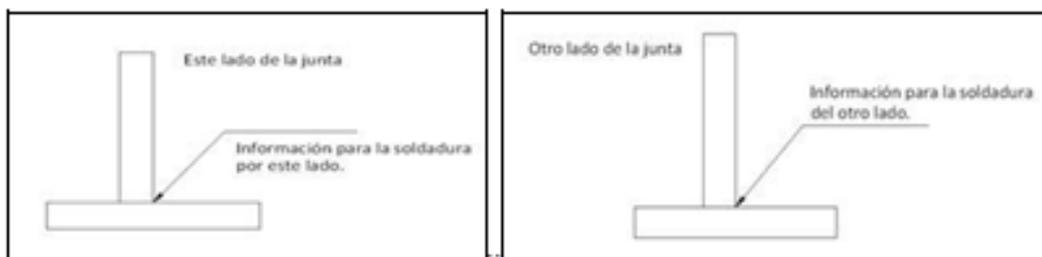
Indicación del lado a realizar la soldadura.
